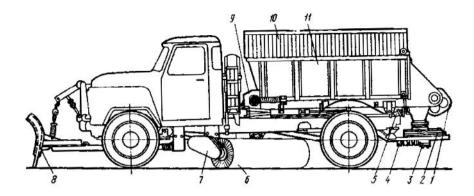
Распределитель противогололедных материалов (пескоразбрасыватель): 1 – редуктор привода конвейера; 2 – разбрасывающий диск; 3 – редуктор диска; 4 – гидромотор привода диска; 5 – гидромотор привода конвейера; 6 – щетка; 7 – цепная передача; 8 – плуг; 9 – конвейер; 10 – решетка; 11 – кузов
